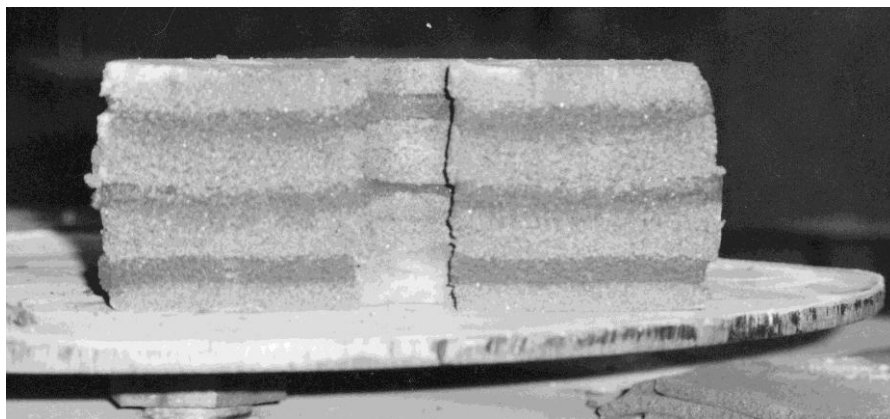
Сечение образца, осаженного между металлическими плитами с покрытием из фторопласта
